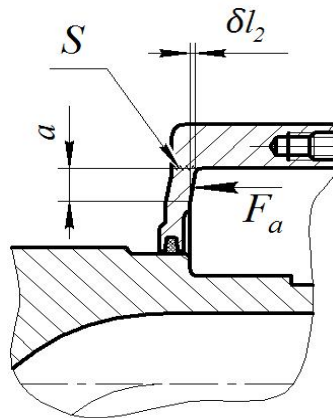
Усилия и перемещения в бурте корпуса, ограничивающего положение подшипника
